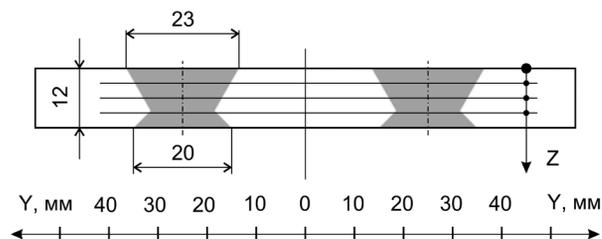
Условная схема поперечного сечения образца сварного шва из сплава 6082
